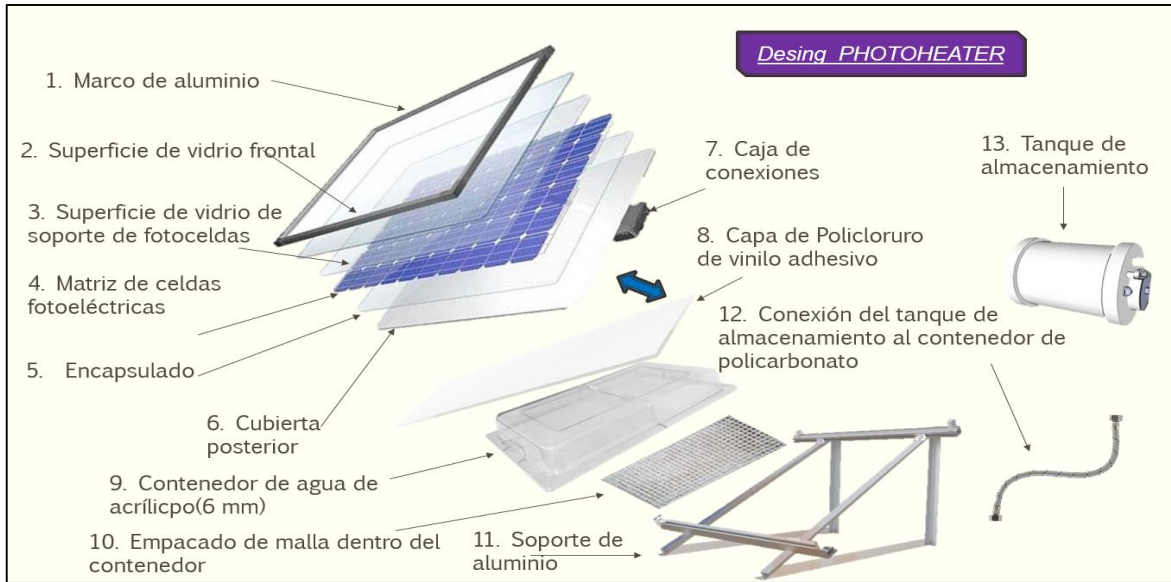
Diseño de la fotocelda con calentador solar integrado.
